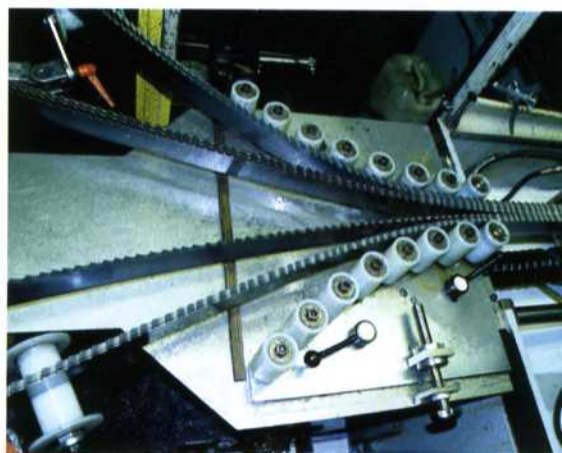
Die Spezialfräsmaschine FS-1000 CNC der Georg Kesel GmbH & Co. KG arbeitet im Längstaktverfahren. Bei der Zuführung werden bis zu 40 abgewickelte Bänder mit bis zu 100 Millimeter Breite kompakt geführt und sicher gehalten
